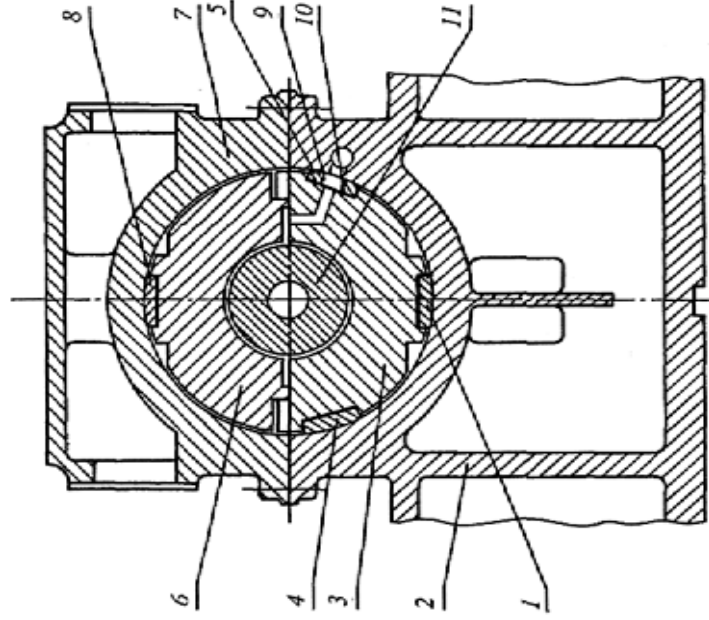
Установка вкладыша опорного подшипника в корпусе: 1, 4, 8 – регулируемые опорные колодки; 2 – корпус подшипника; 3 – нижняя половина вкладыша; 5 – регулируемая опорная колодка с отверстием маслопровода и дроссельной шайбой; 6 – верхняя половина вкладыша; 7 – крашка корпуса подшипника; 9 – канал маслопровода; 10 – регулируемая подкладка; 11 – опорная шейка ротора
